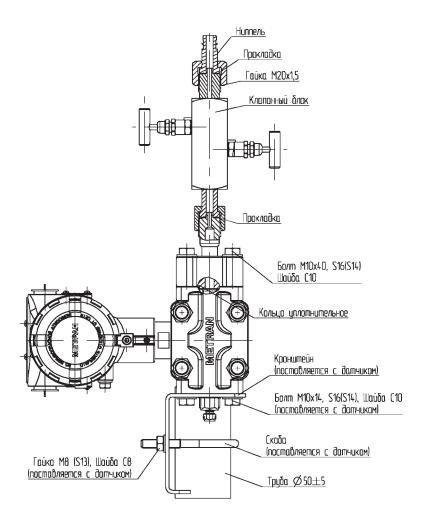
Вариант установки клапанного блока 0106 М Т для датчиков типа Метран-150CG. Габаритные и присоединительные размеры см.рис.21.
